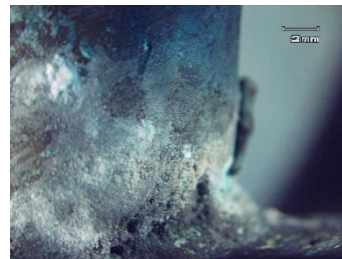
Solda não retificada e superfície porosa parte interior perna dianteira direita
